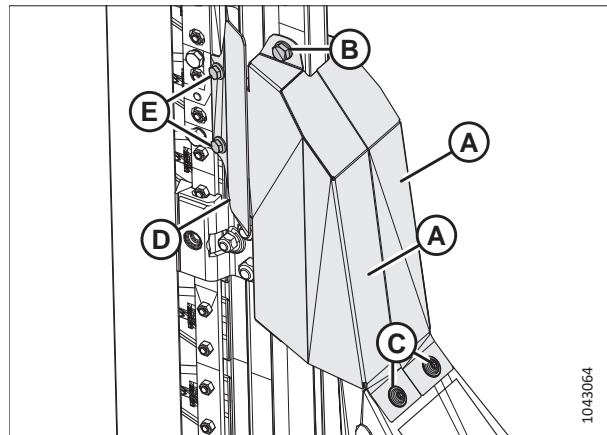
Wiedereinbau der Befestigungselemente um das Messer
